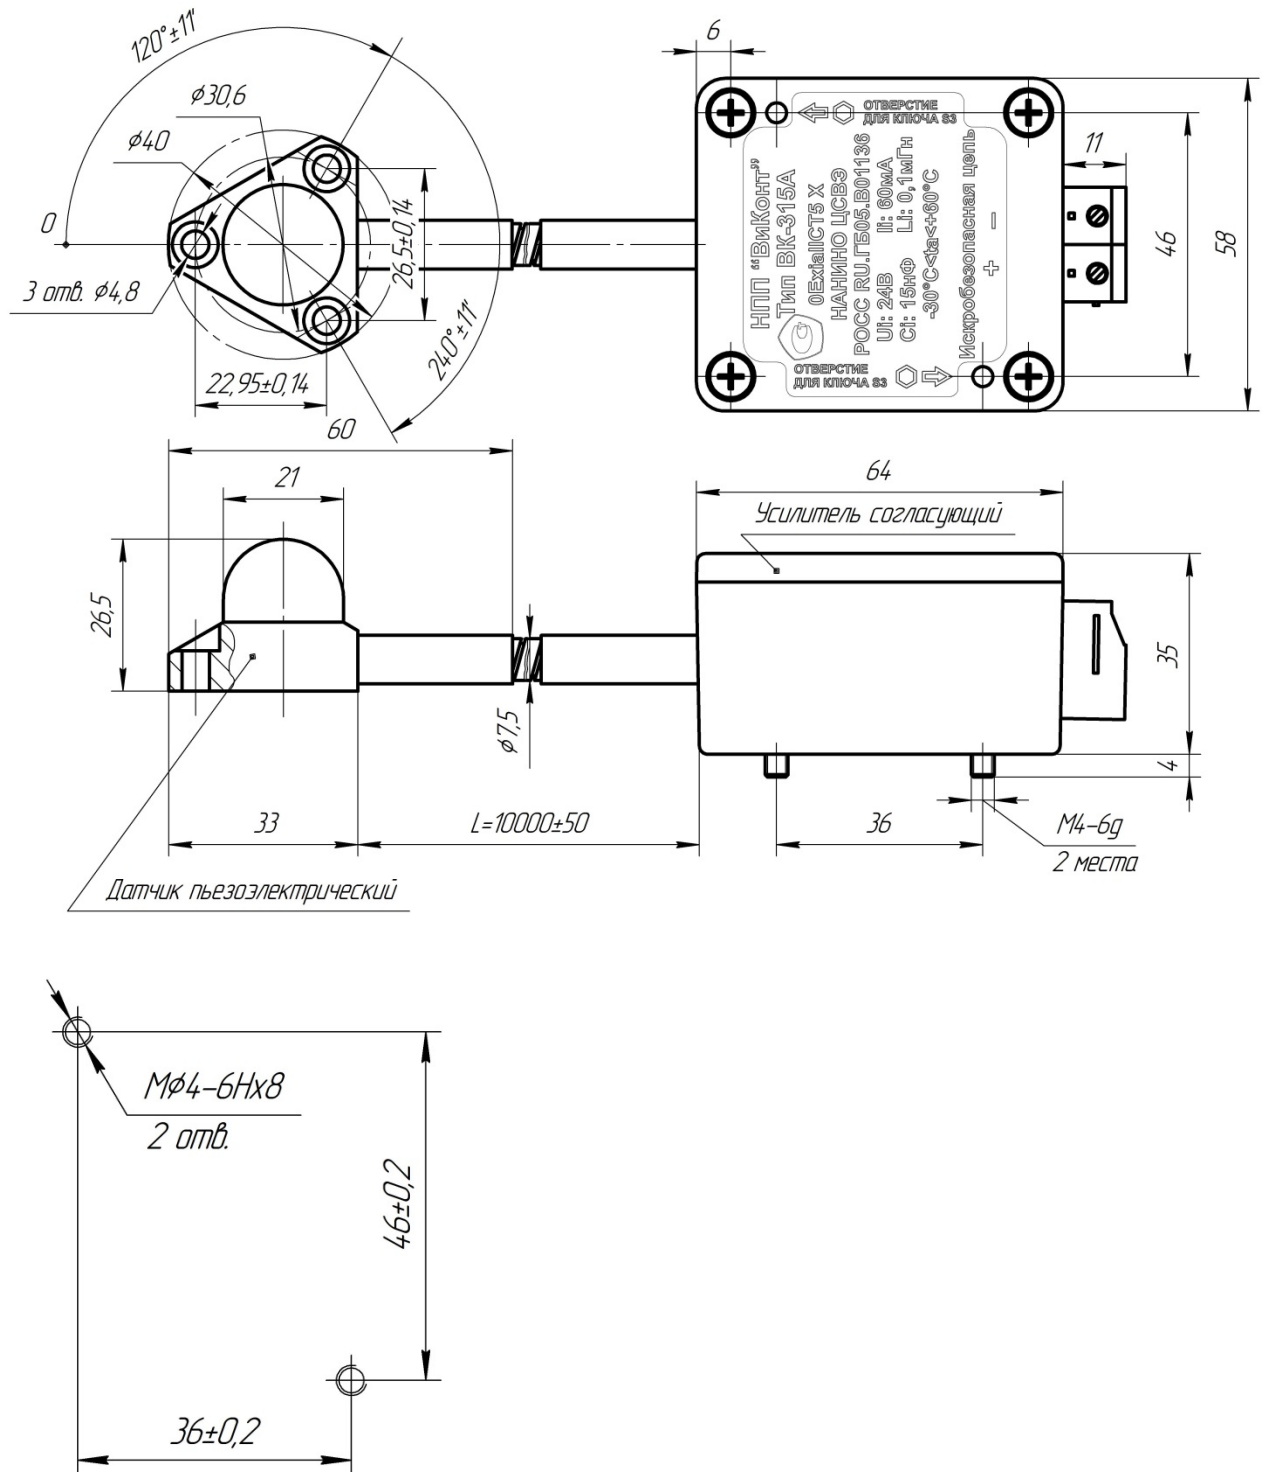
б. Установочные размеры для предусилителей вибропреобразователей ВК-312 и ВК-315А
